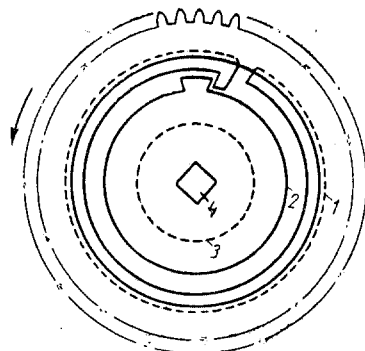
Приспособление для проскальзывания заводной пружины фирмы Movado Co; 1 — скользящая пружина; 2 — заклепка на заводной пружине.
